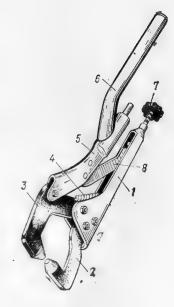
1— корпус; 2— губка нижняя; 3— губка верхняя; 4— пружина растяжения; 5— кожух; 6— ручка; 7— винт регулировочный; 8— упор
